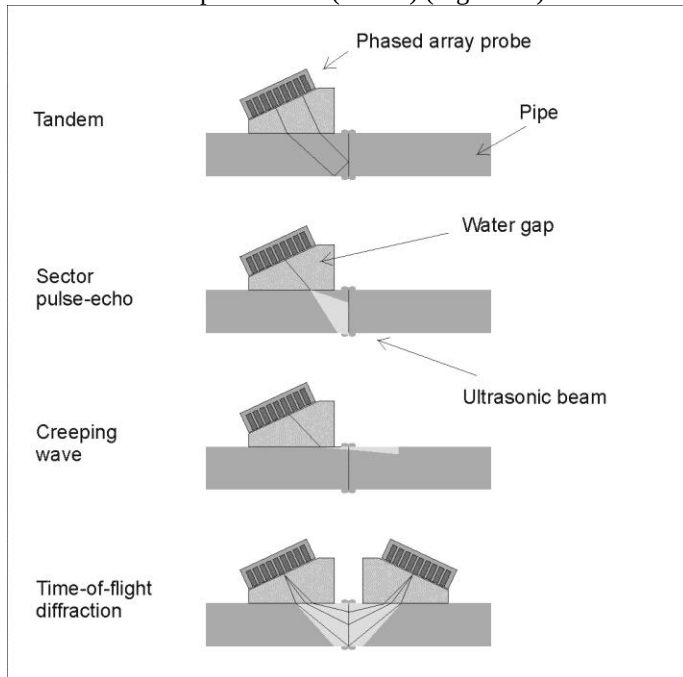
TÉCNICAS DE INSPECCIÓN UTILIZADAS PARA LA INSPECCIÓN DE SOLDADURAS BF
